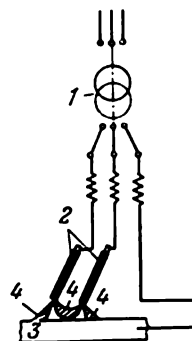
Schéma du soudage à l'arc triphasé
